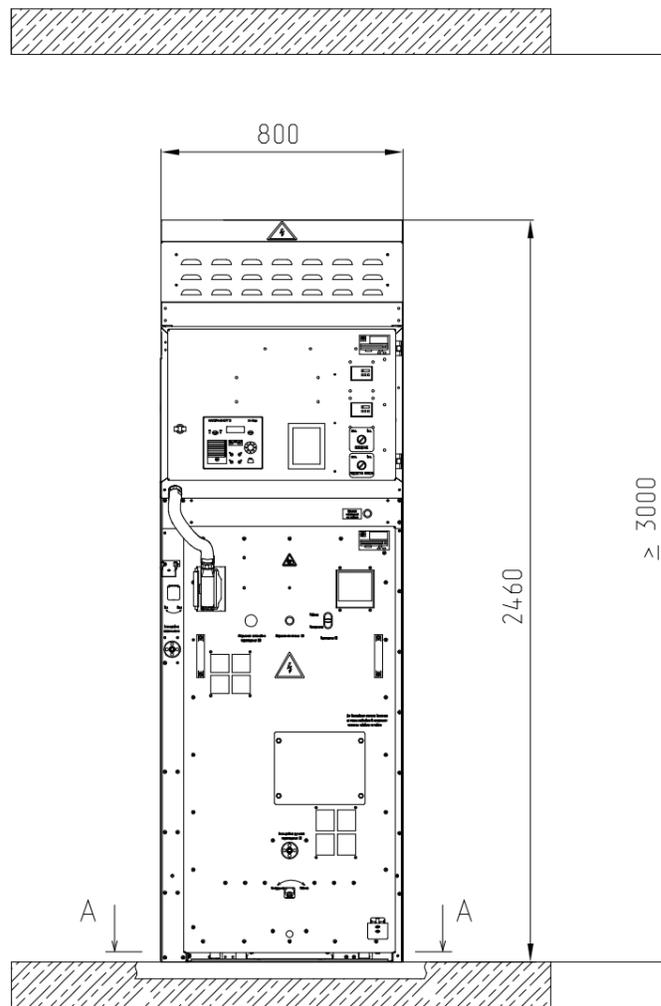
Ячейка фидера КВ-825-Ф-УХЛ4, ячейка резервного выключателя КВ-825-РВ-УХЛ4
